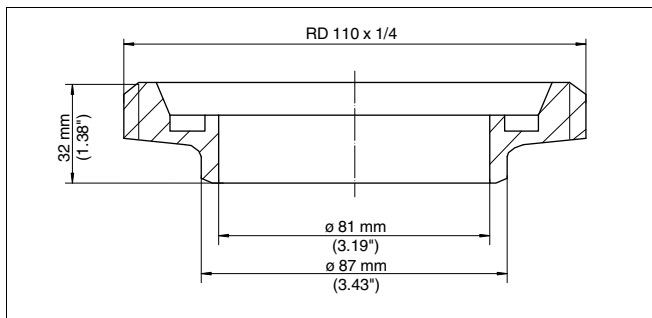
Размеры приварного штуцера - накидная гайка DN 80 по DIN 11851
